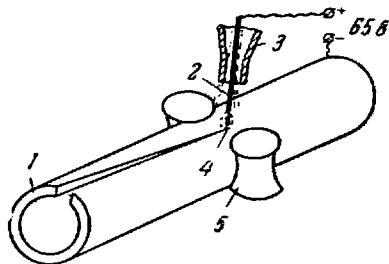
Схема дуговой электросварки труб с защитой дуги инертным газом
